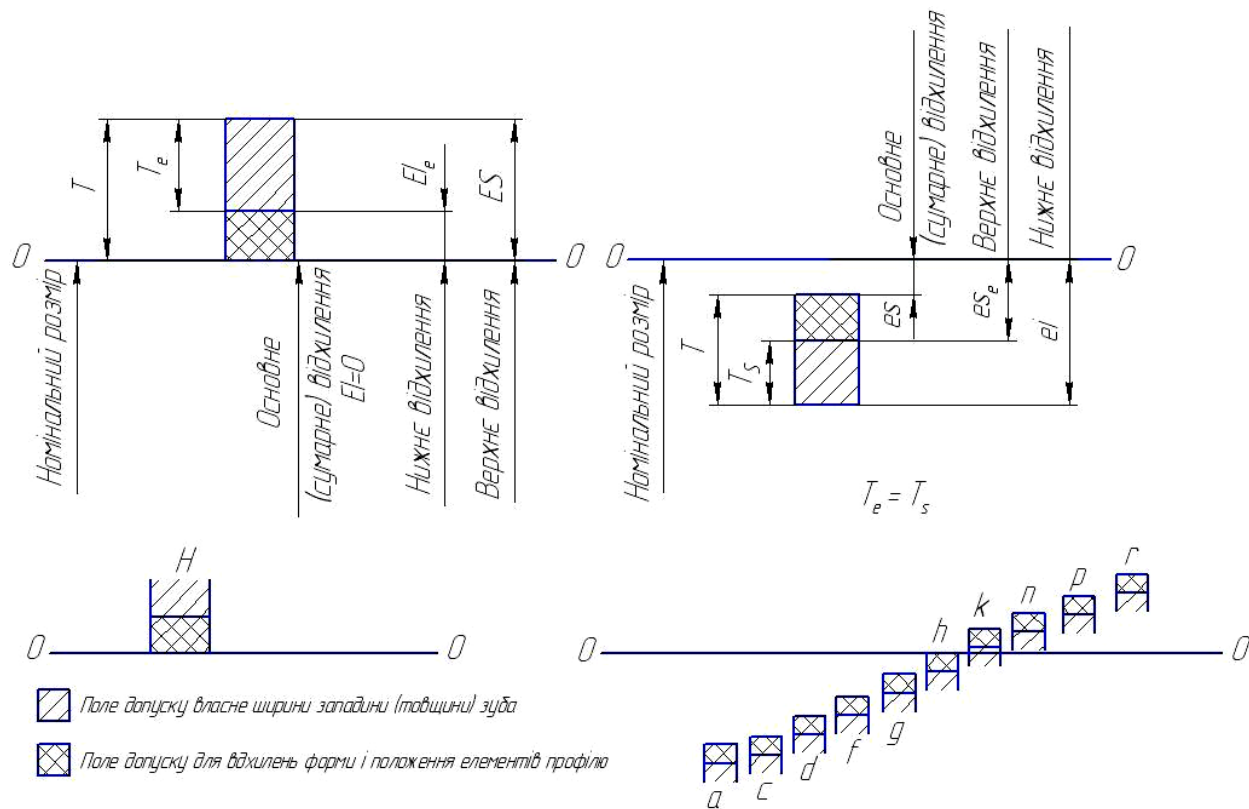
Розташування полів допусків ширини западини і товщини зуба
